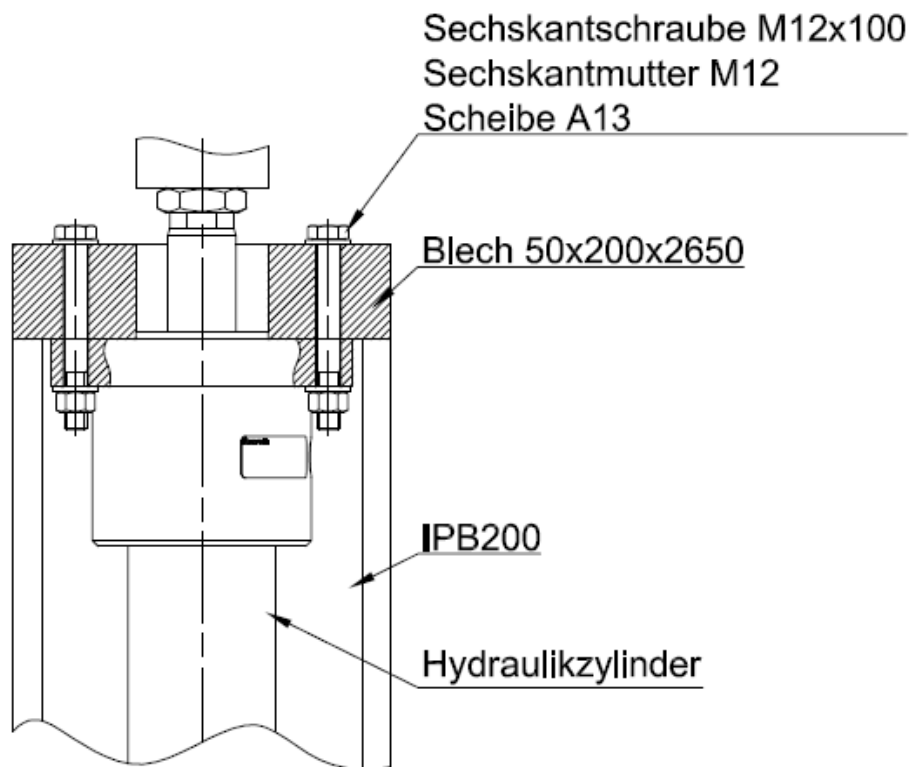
BG5; Detail Befestigung Hydraulikzylinder
